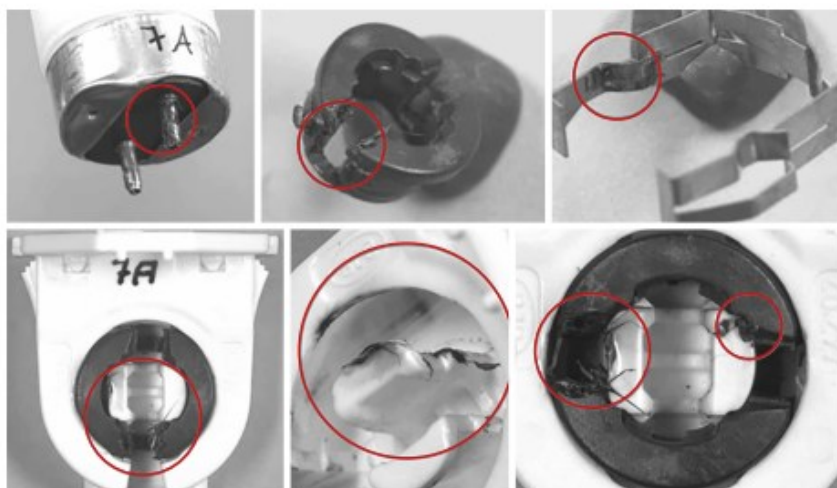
Beschädigte Fassungen, in denen Retrofit-Lampen mit zu hohem Gewicht betrieben wurden
